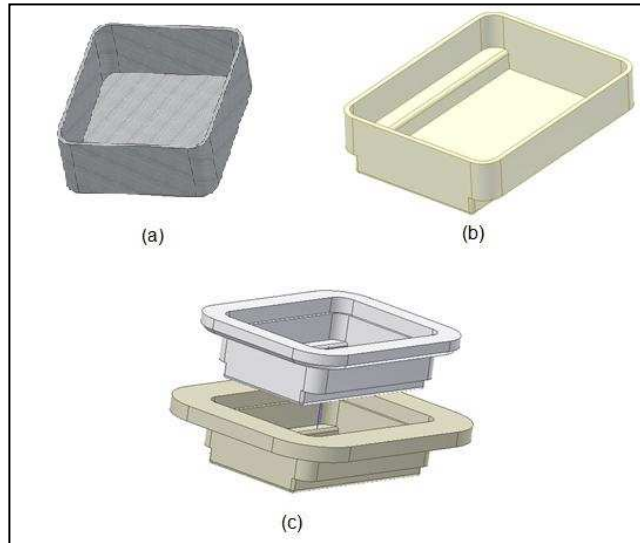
(a) diseño normal, (b) diseño final del prototipo, (c) molde macho-hembra.
